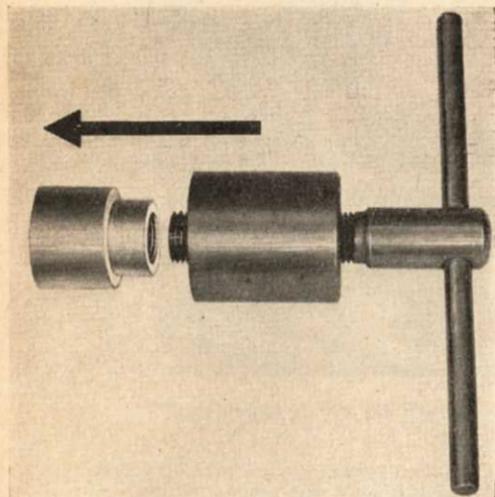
Position de la bague 1.141 pour montage des joints d'étanchéité avec l'outil 1.050
